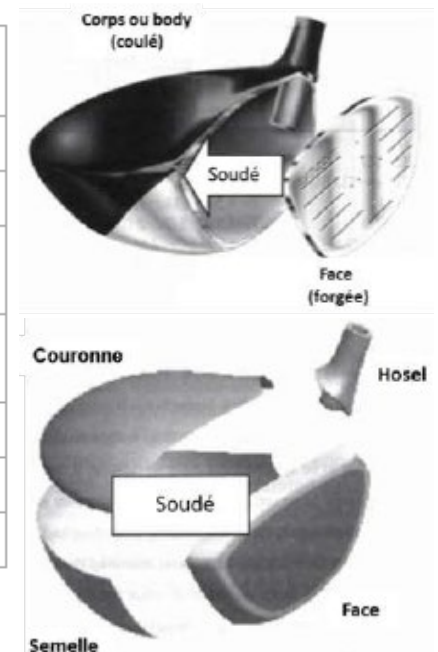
Drivers à corps moulé ou formé à froid puis soudé. [2]
